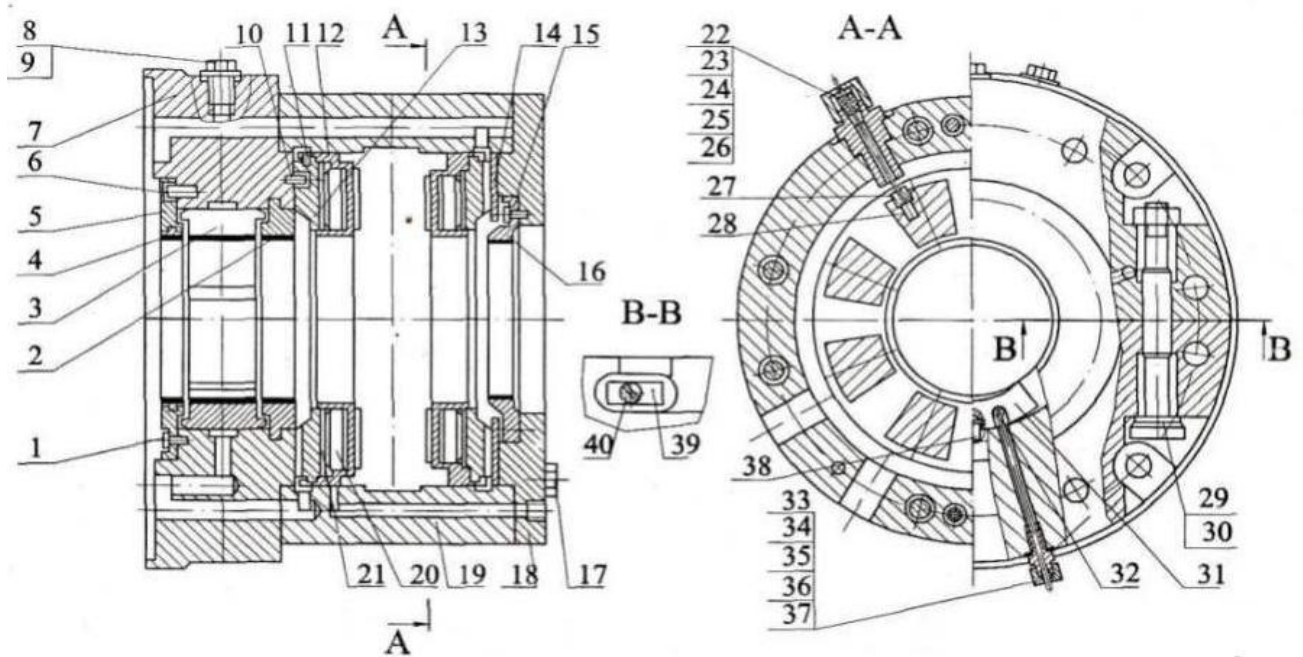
Вузол – опорно-упорний підшипник
